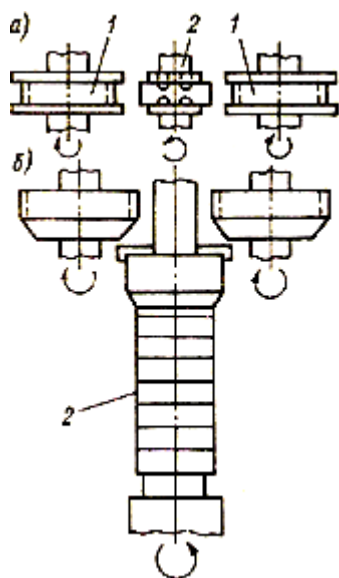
Схема накатки: а-штучных заготовок, б-от прутка; 1-деформирующий инструмент; 2-заготовка.
